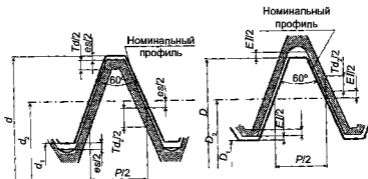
Схемы расположения полей допусков наружной и внутренней резьбы в посадках с зазором
